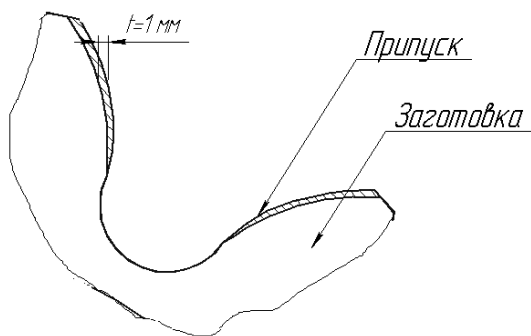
Схема реализации предварительного фрезерования зубьев венца колеса движителя БСП
